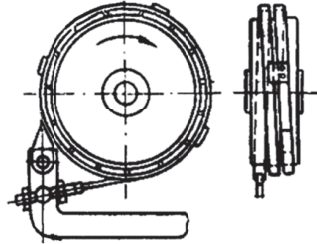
Простой ленточный тормоз с несколькими витками ленты
